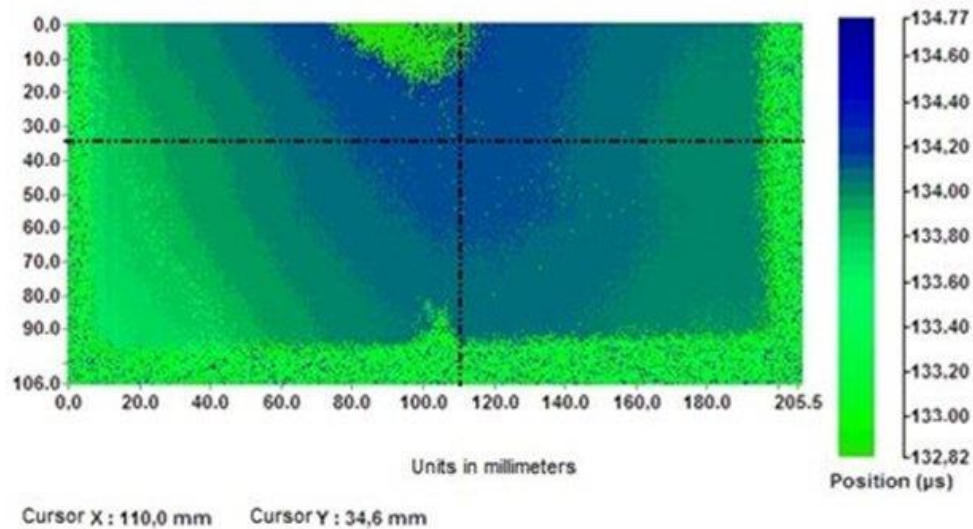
Image ultrasonique C-scan du troisième échantillon d'acier (10 × 20 cm) contenant des défauts de surface sous forme de piqûres de corrosion et de défauts de soudure ((Position (µs)).
